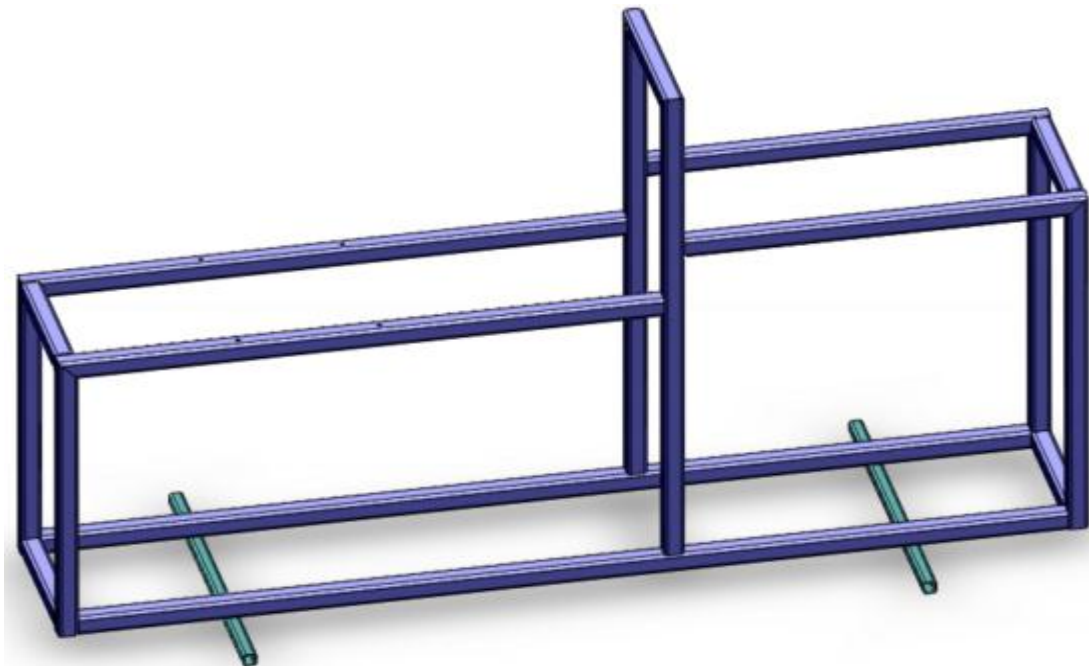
Modelo en 3D del chasis del prototipo de la máquina para expandir.
